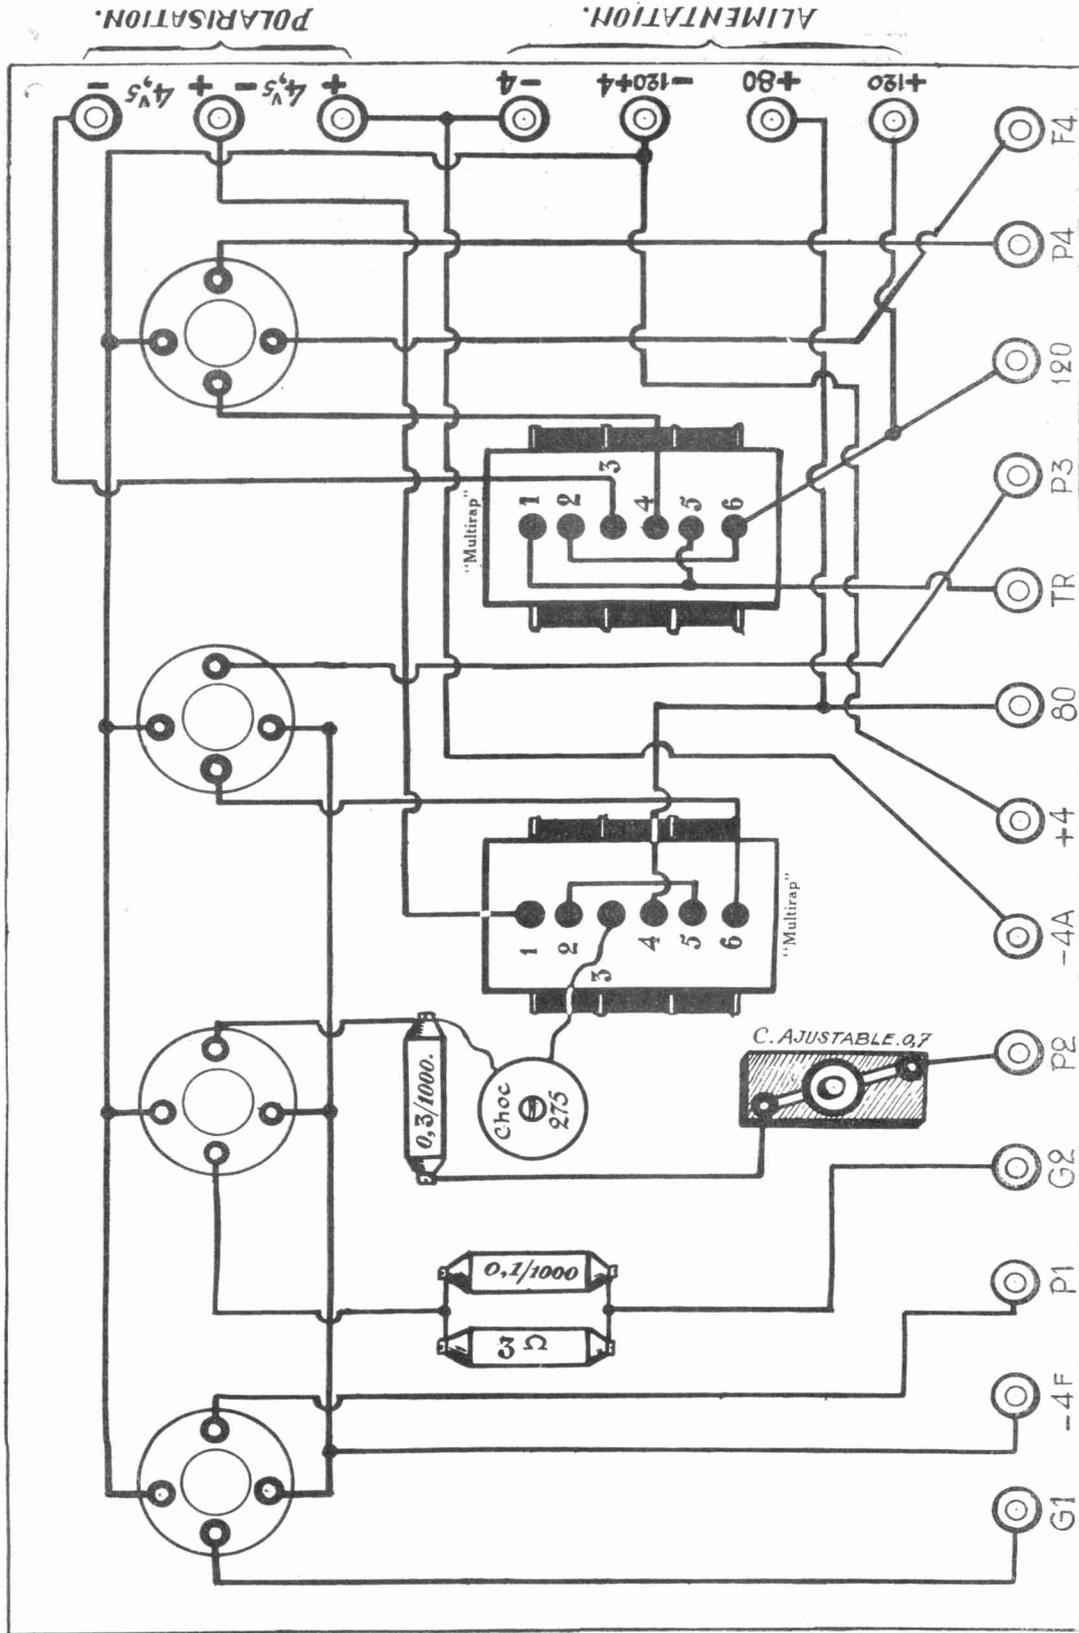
Plan de câblage de la plaque à lampes (réduction du plan grandeur naturelle).
